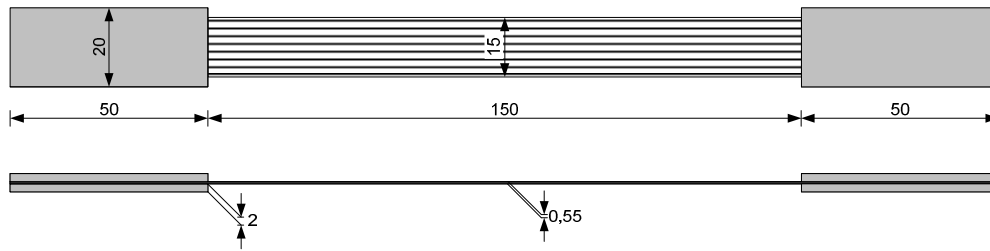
Dimensões dos corpos-de-prova de CFC ensaiados (dimensões em mm).
